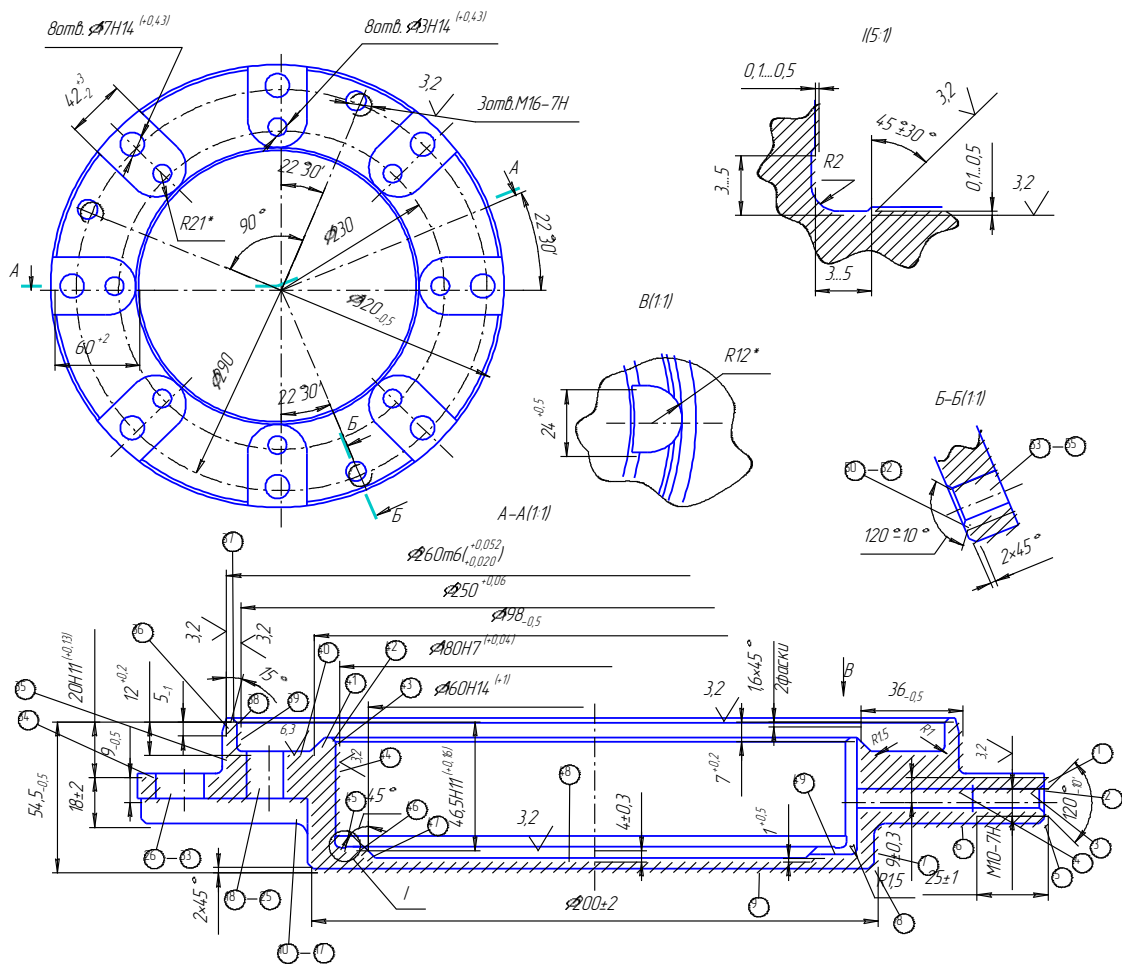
Ескіз деталі з винесеними поверхнями.
